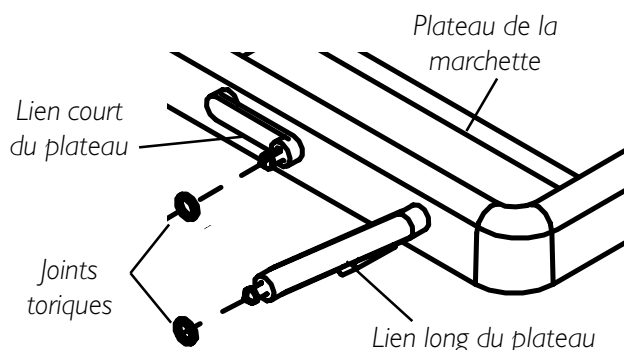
INSTALLER LES JOINTS TORIQUES SUR LES LIENS DU PLATEAU
